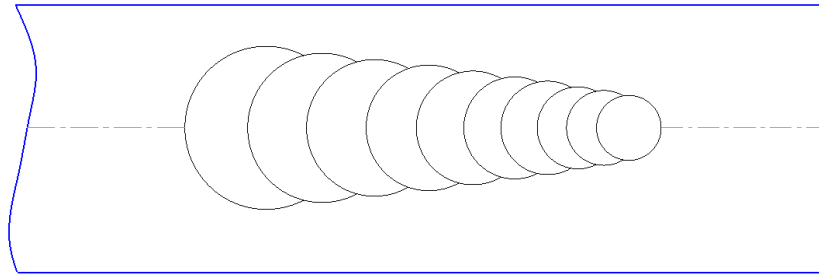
Эскиз сварного соединения при импульсной сварке
